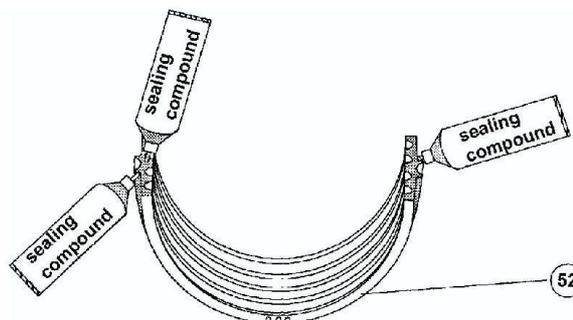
Revêtement de pâte d'étanchéité sur la chicane flottante.
